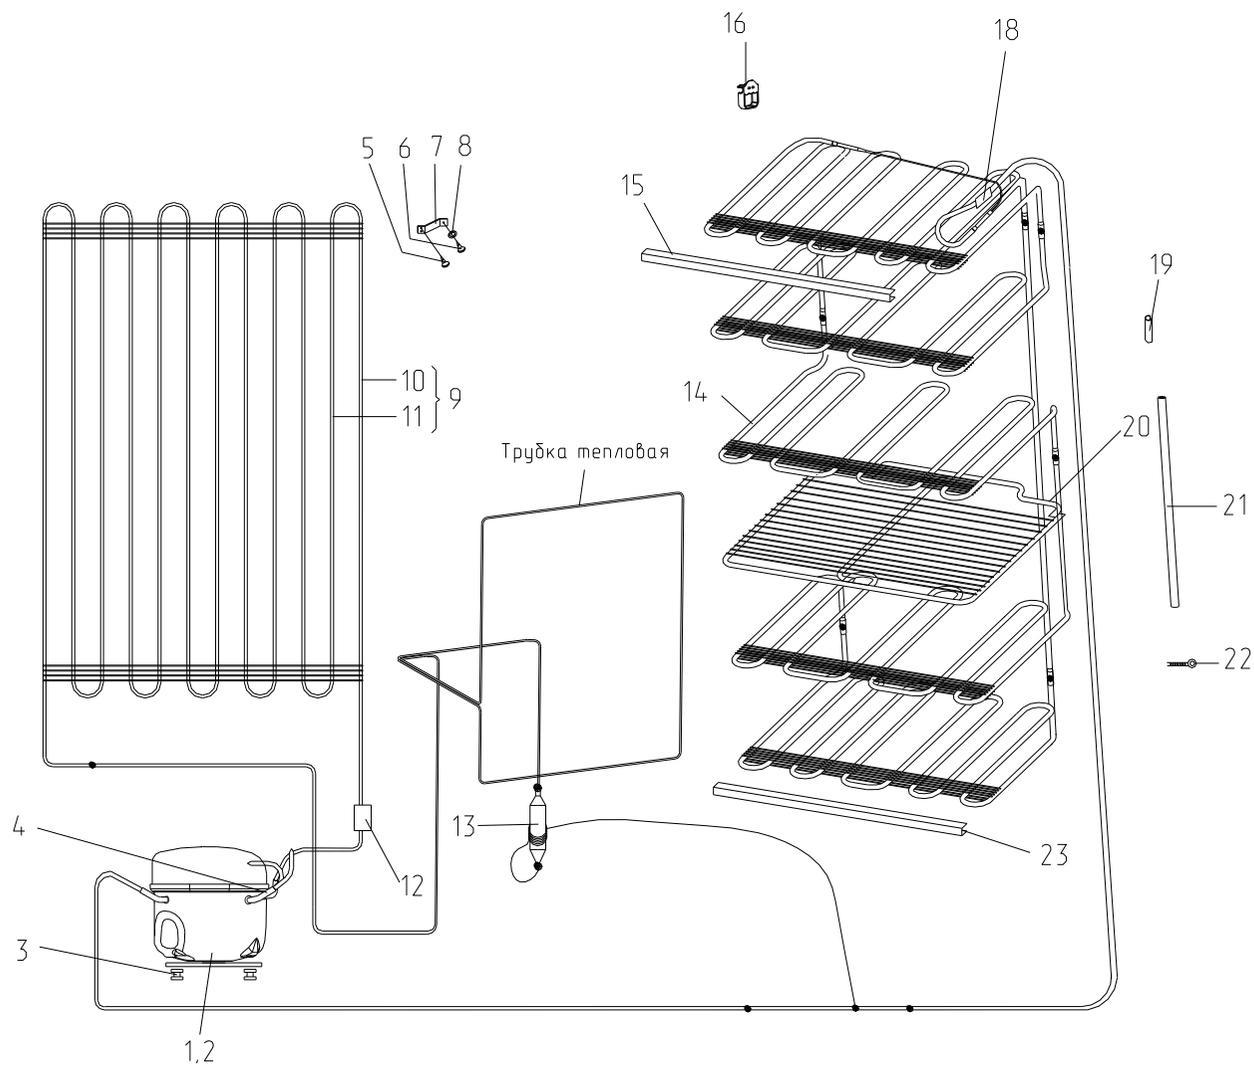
Схема холодильного агрегата с компрессорами СТС и СТВ
